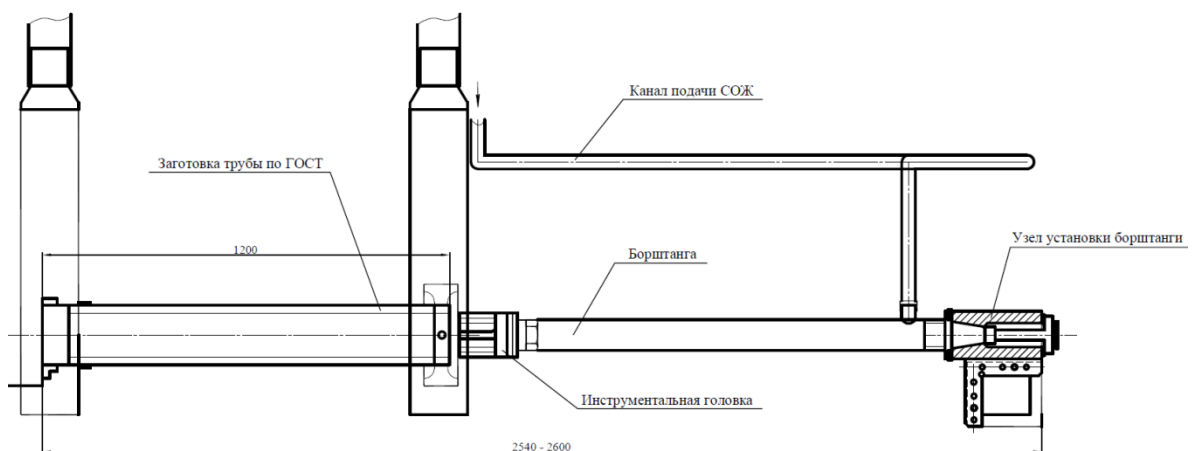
Схема обработки заготовок гидроцилиндров
